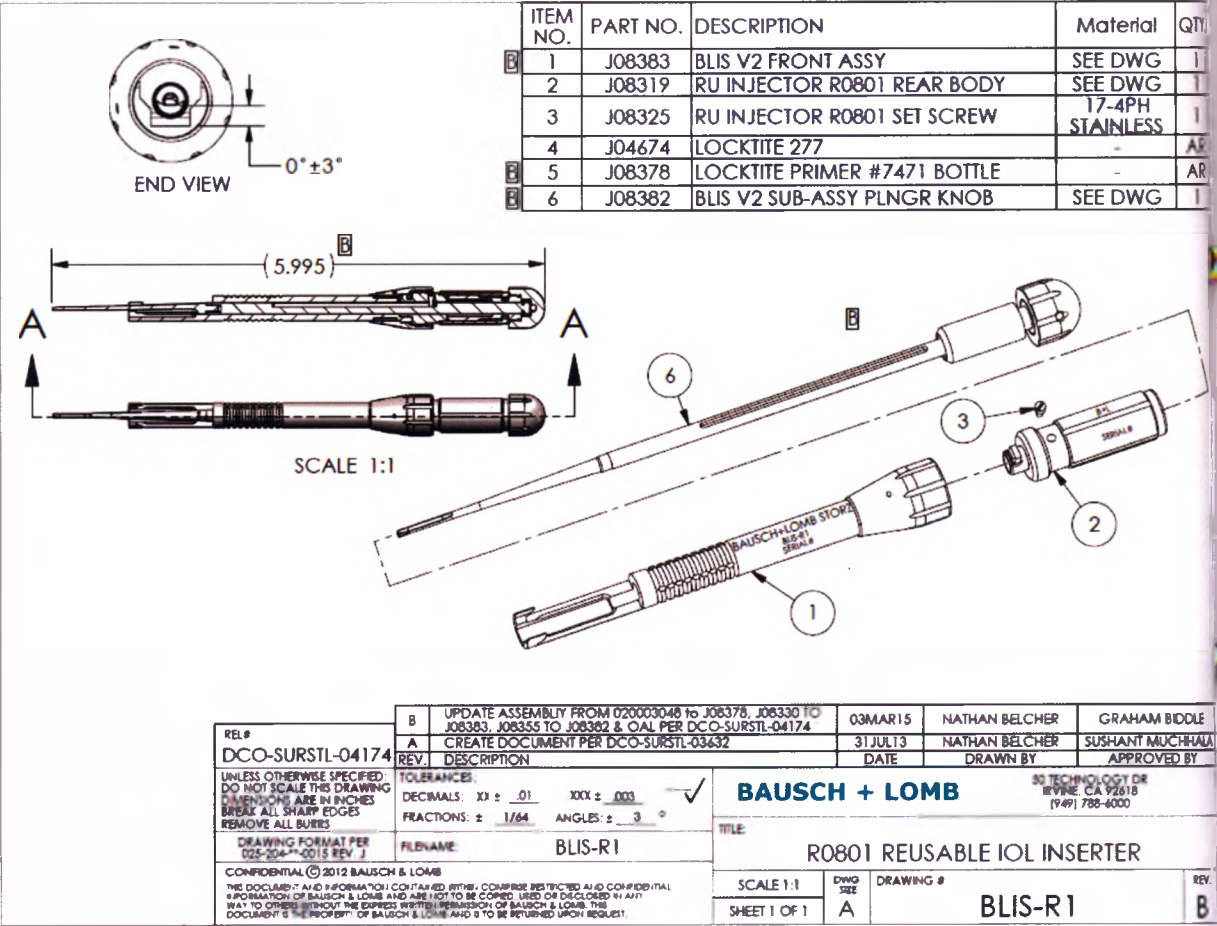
Оригинальный чертеж рукоятки BLIS-R1 с габаритными размерами, размеры указаны в дюймах:
